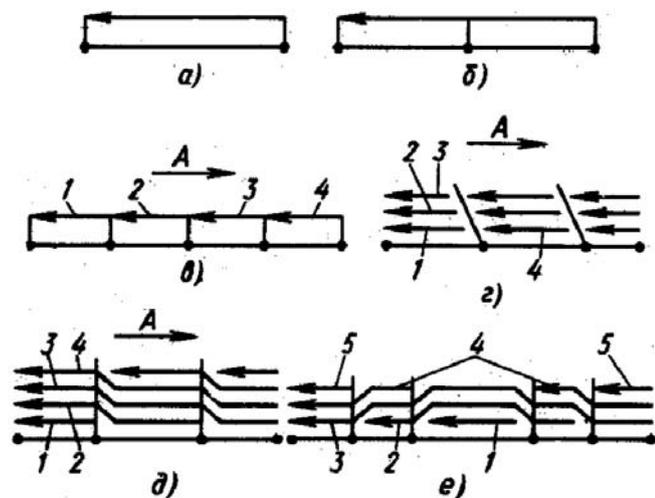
Сварка швов: а – напроход; б – от середины к концам; в – обратно-ступенчато; г – блоками; д – каскадом; е – горкой; А – направление заполнения разделки; стрелками указаны последовательность и направление сварки в каждом слое (1 – 5)
